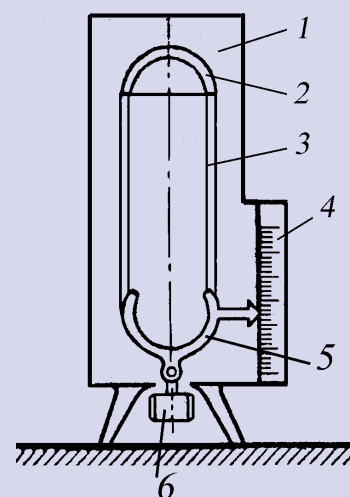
Схема приспособления для калибровки клиновых ремней
